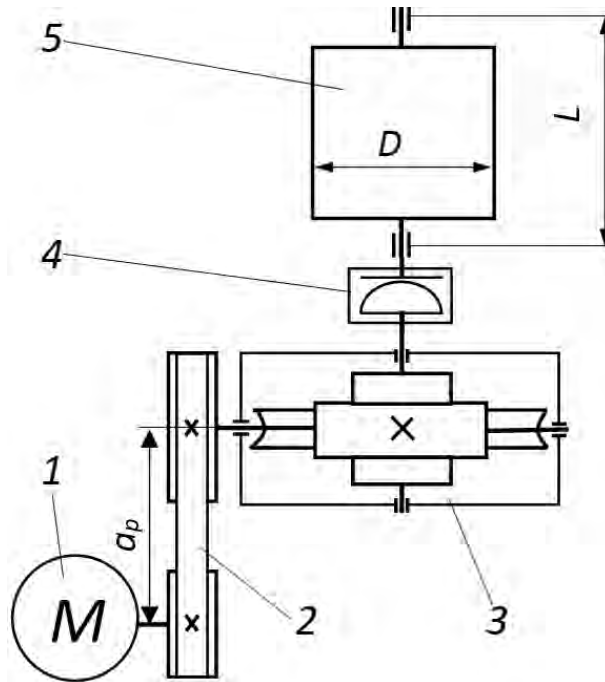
Схема привода грузоподъемного механизма (вид сверху): 1 – асинхронный электродвигатель; 2 – клиноременная передача; 3 – редуктор червячный с верхним расположением червяка; 4 – муфта зубчатая; 5 – приводной вал с барабаном
